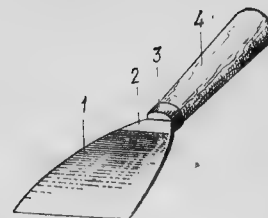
1 — полотно; 2 — накладка; 3 — колпачок; 4 — ручка
